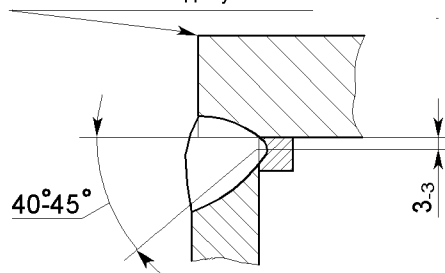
Разделка сварного шва приварки полки лонжерона
